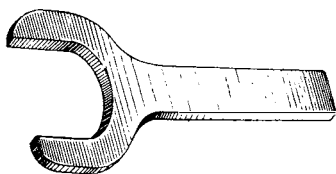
Ключ 48030-1-003МД для шаровой гайки кулисы
